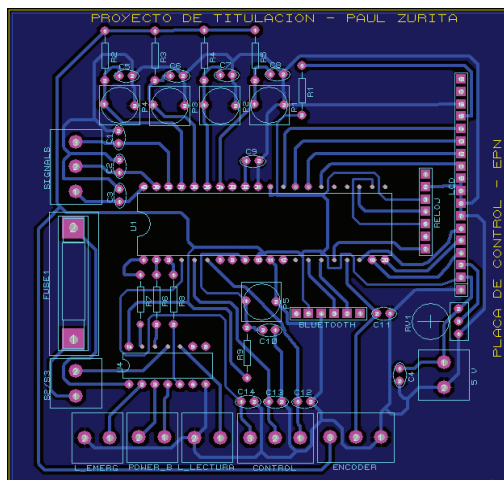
PCB en ARES de Proteus 7, placa de control.
